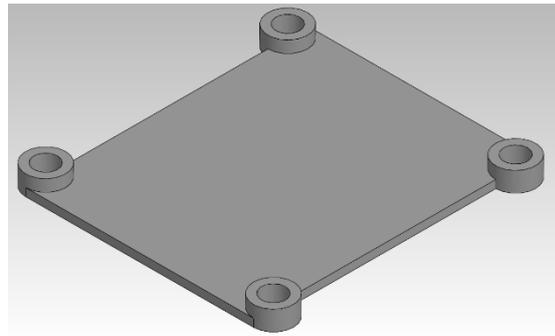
Общий вид 3D-модели держателя отладочной платы.
